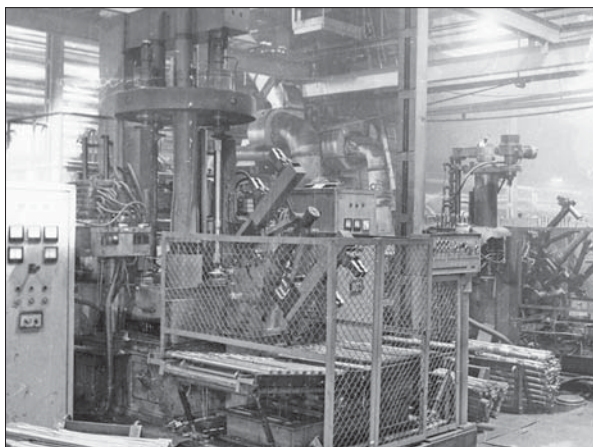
Карусельний верстат-автомат швидкісної термообробки довгомірних деталей трактора «Кіровоць»
